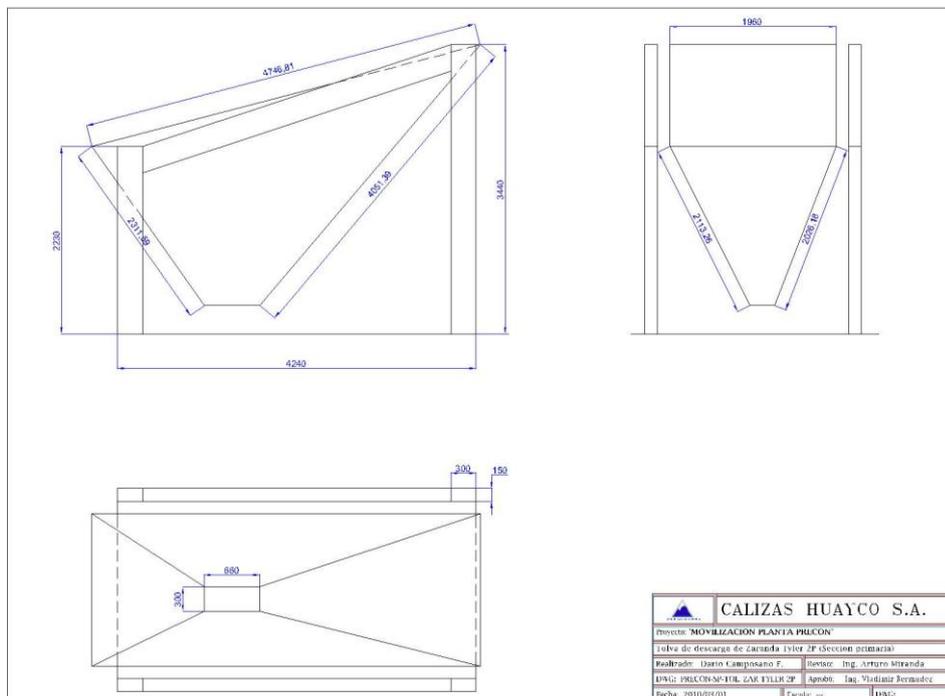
Layout para el montaje de la Planta de Agregados.
